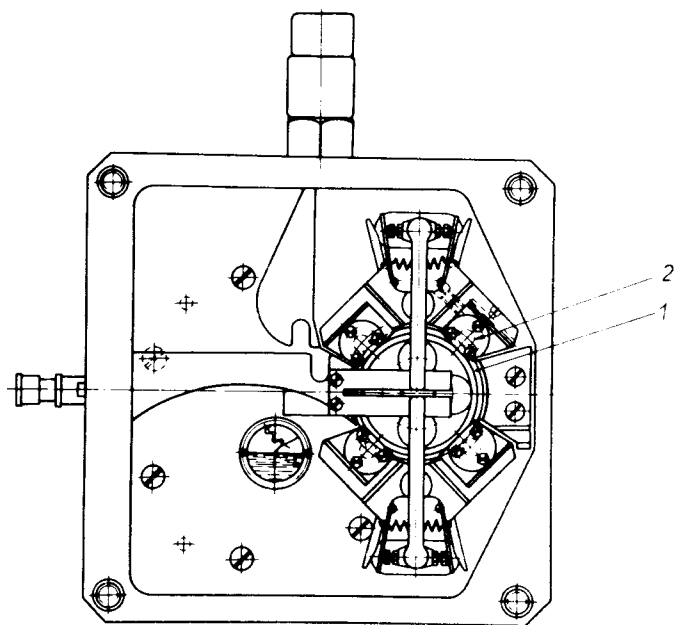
Лентопротяжный механизм - Вид А. 1 - обрешиненный барабан, 2 - прижимные ролики.
